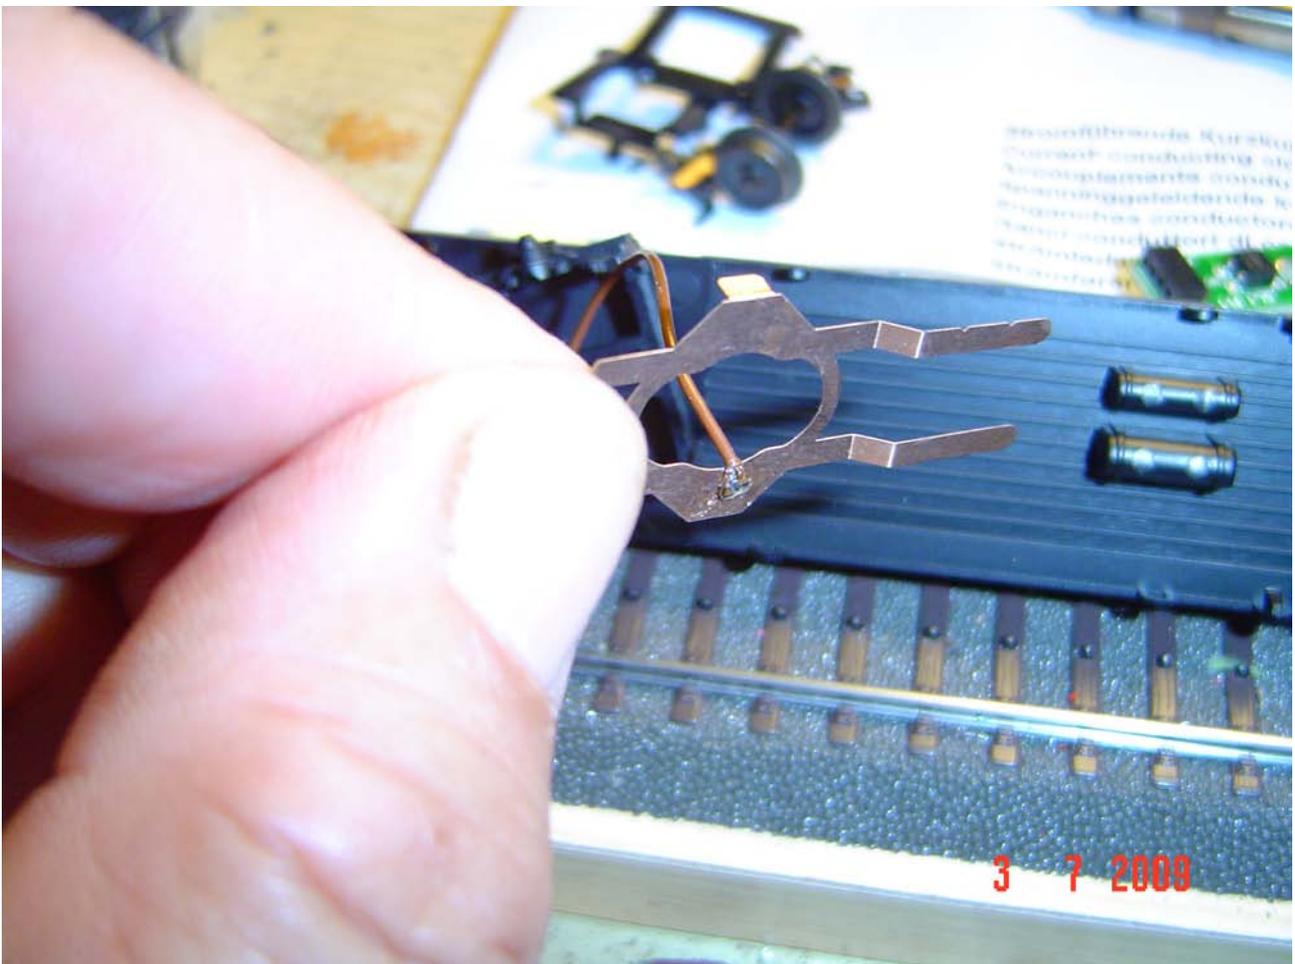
la lamella di massa e la particolare posizione del cavetto
